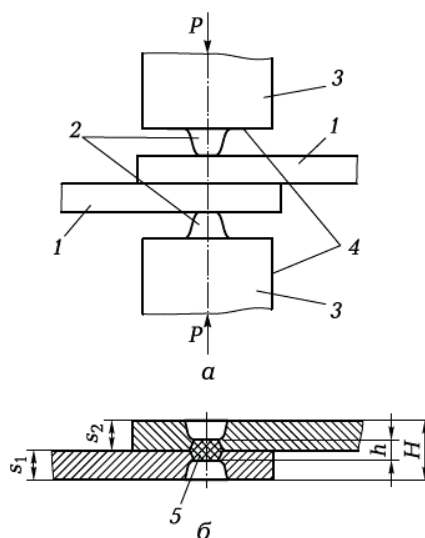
Схема холодной сварки (а) и геометрия сварного соединения (б) [5].
